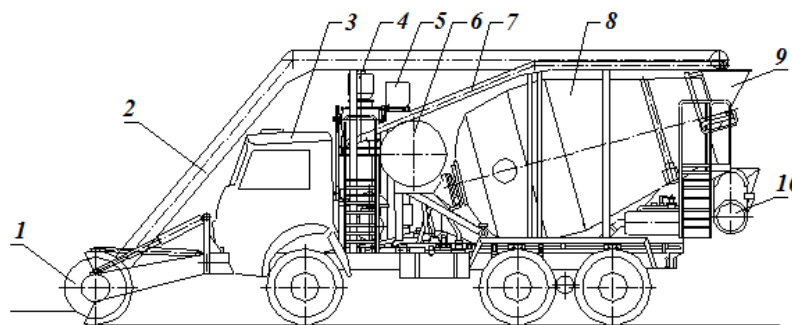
Мобильная установка рекультивации почв: 1 - фрезерный рабочий орган; 2 - транспортер перемещения нефтезагрязненной почвы; 3 - шасси базового автомобиля КамАЗ-5511; 4 – измельчитель; 5 - бак для биопрепарата; 6 - бак для моющей жидкости; 7 - транспортер перемещения препарата; 8 - перемешивающий барабан; 9 - загрузочный лоток; 10 - разгрузочные лотки.
